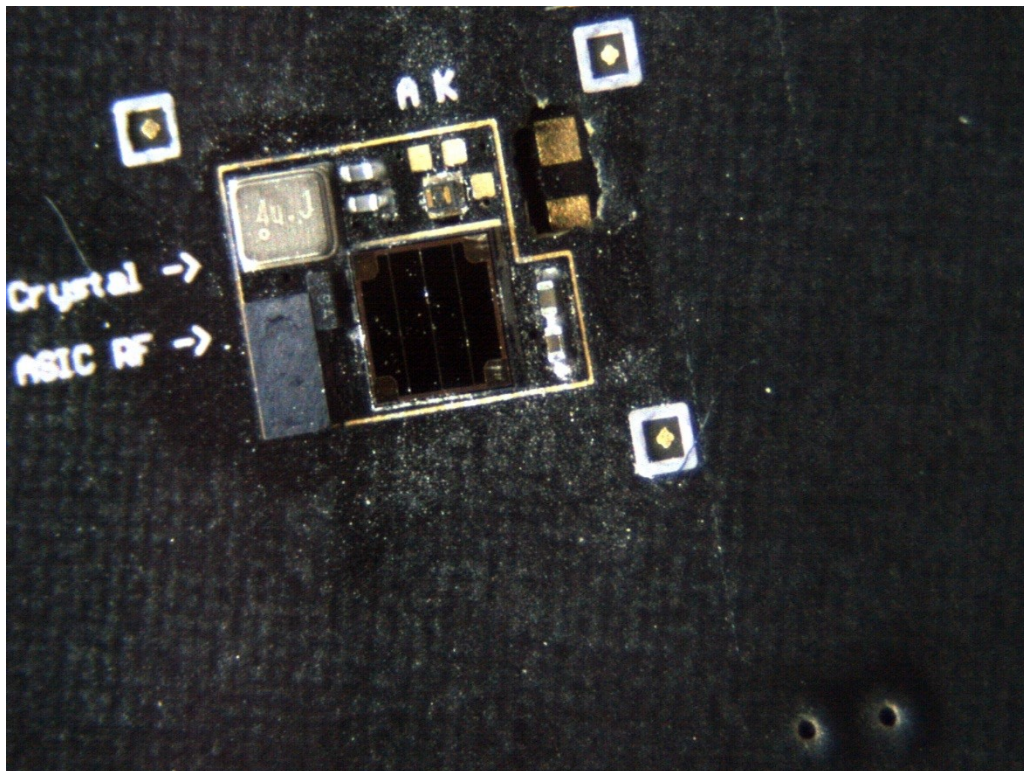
Composantes assemblées sur la face de dessus du PCB interposeur
